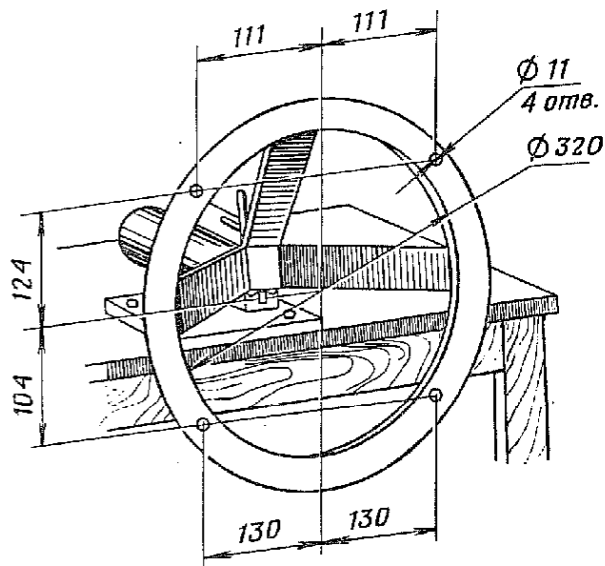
Приспособление для крепления двигателя при разборке и сборке
